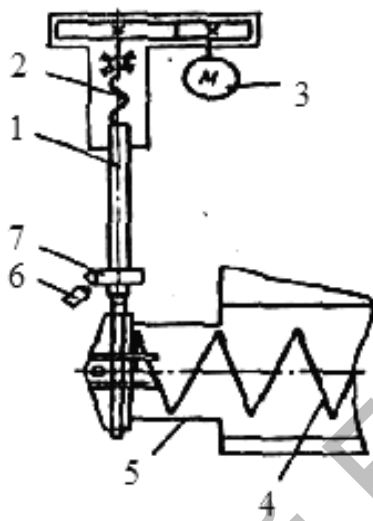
Схема привода шибера выгрузного шнека смесителя:
